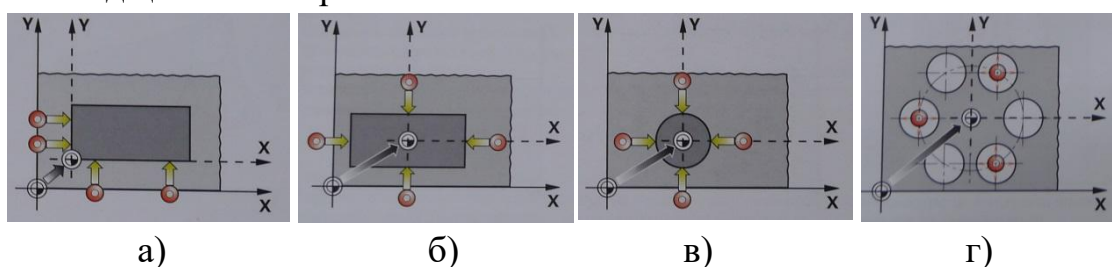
Визначення опорних точок для за допомогою вимірювального щупа: а – зовнішній кут; б – центр прямокутної заготовки; в – центр циліндричної заготовки; г – центр отворів, виконаних по колу
